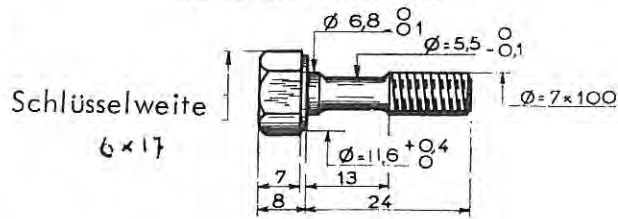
Anschlussschraube MR-3705 für Öldruckmessung
